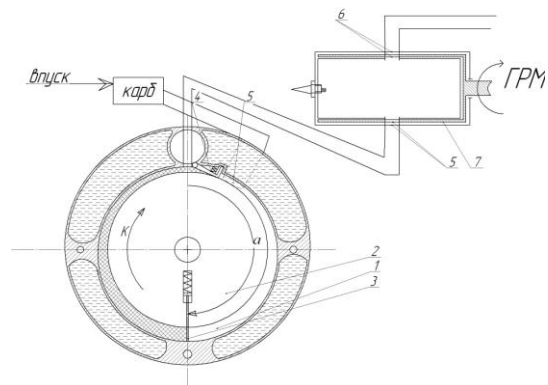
Сжатие рабочей смеси в рабочей полости компрессора
